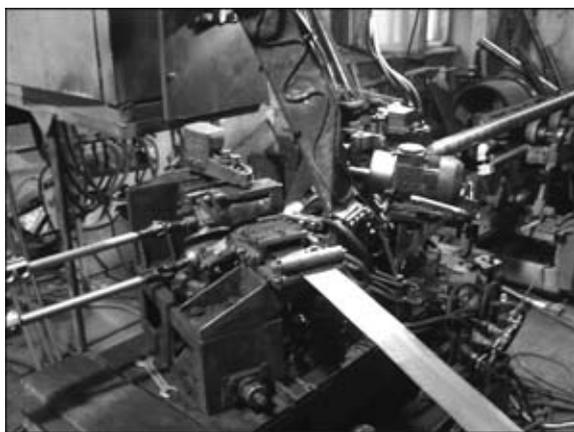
Формовочно-сварочное устройство для производства спиральношовных труб
